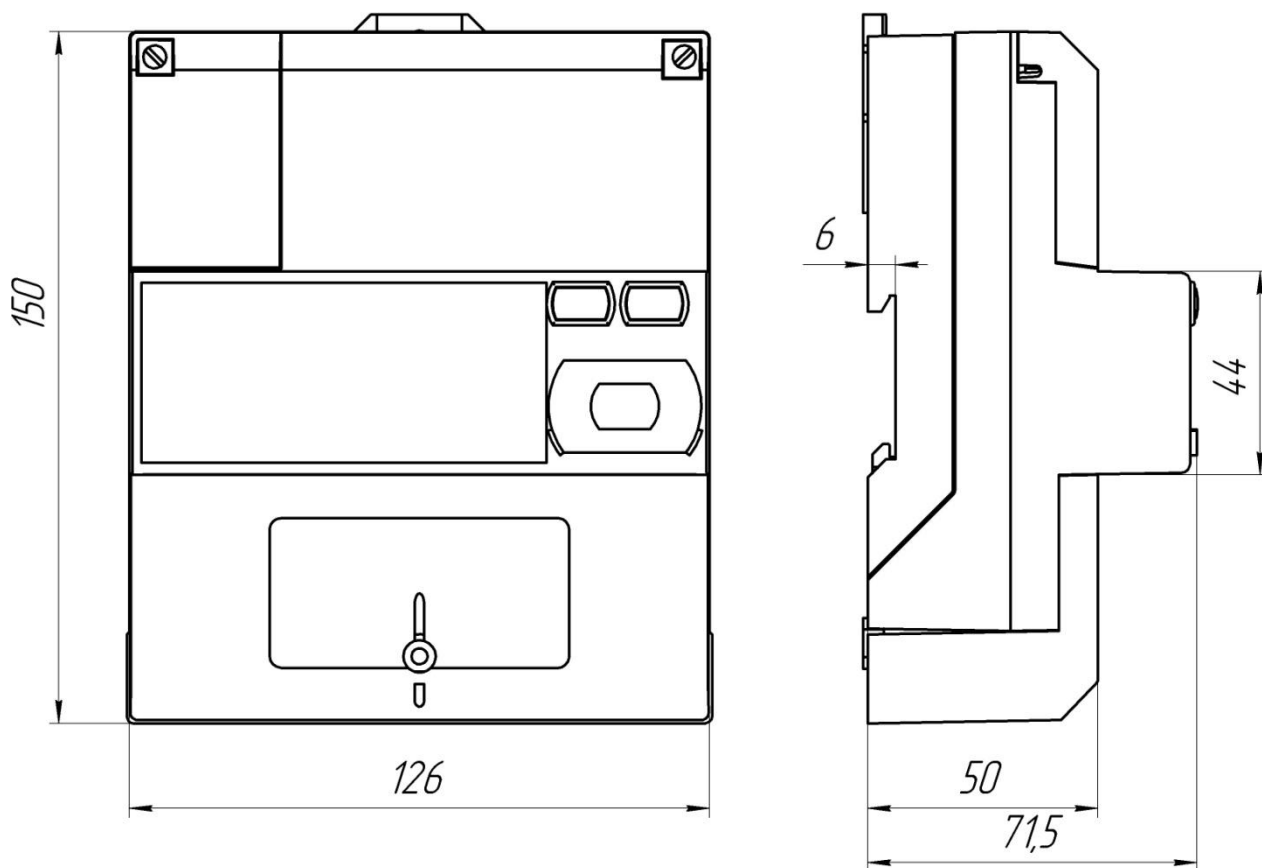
Габаритный чертеж и установочные размеры счётчиков для установки на DIN-рейку СЭБ-1ТМ.04Т.60 – СЭБ-1ТМ.04Т.63
